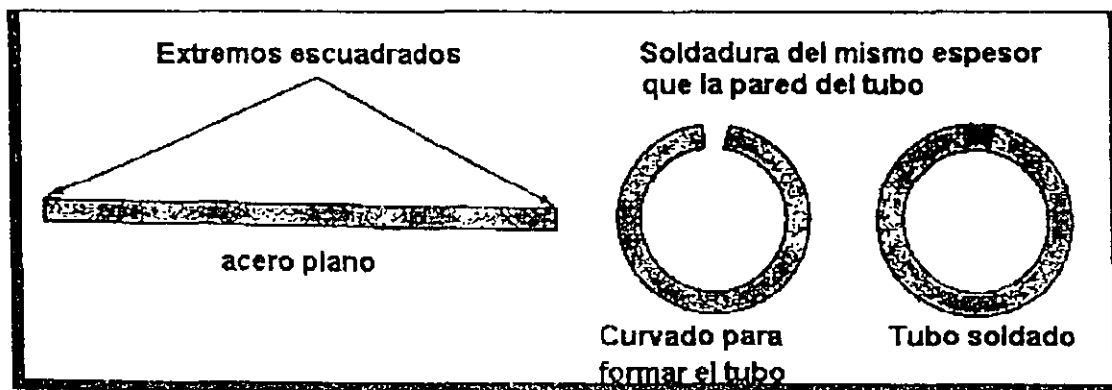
Esquema de fabricación de tubo soldado a tope
